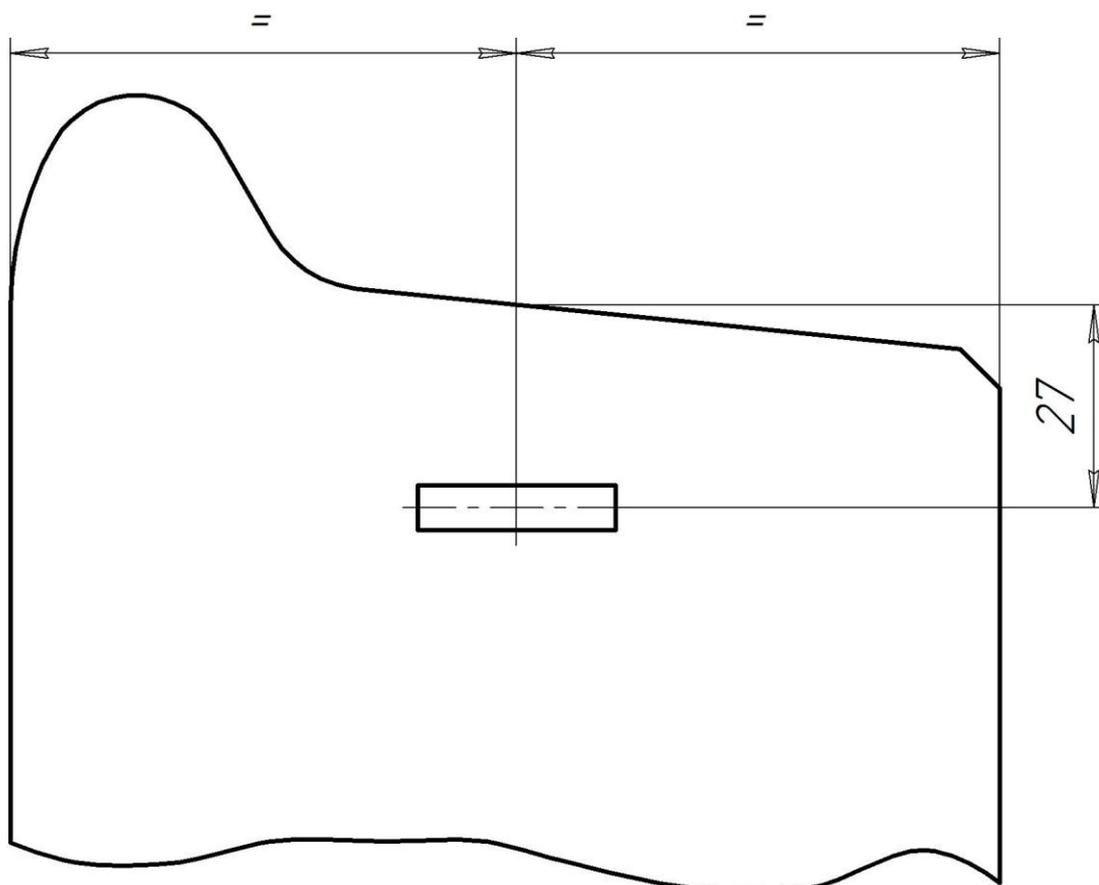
Схема вырезки образцов из обода колеса для испытания на контактно-усталостную выносливость
